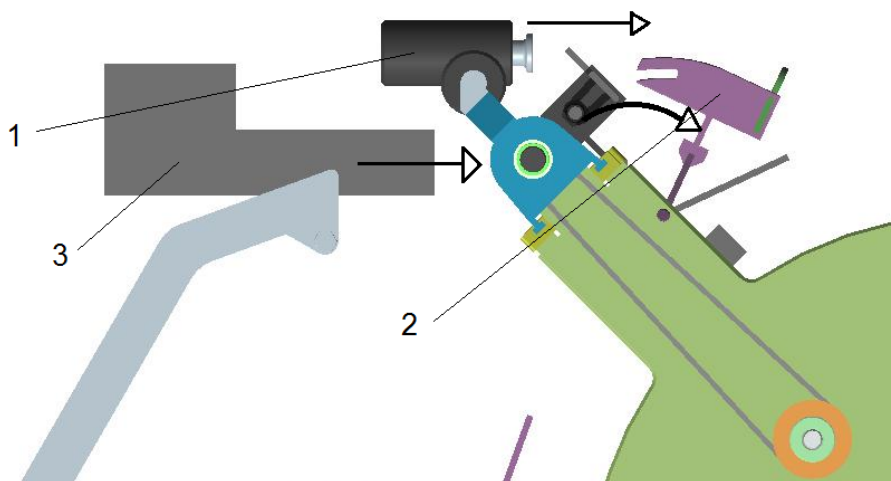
sklopení zajištění pomocí pneumatického mechanismu
